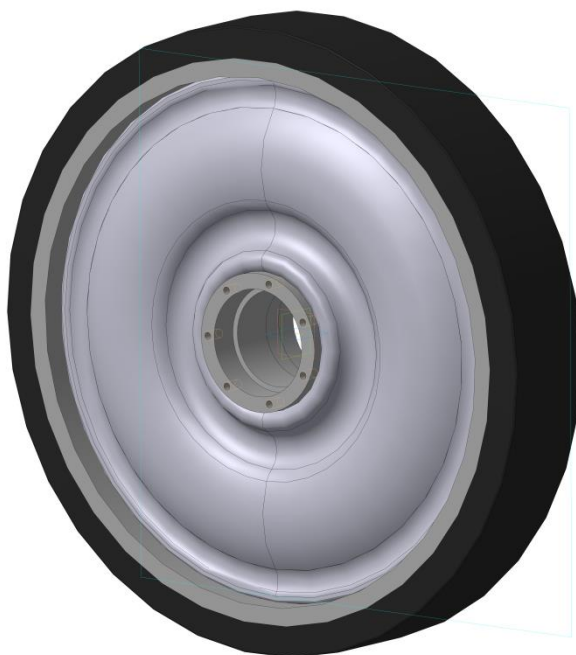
3D-модель изделия «Каток опорный» с резиновой шиной
